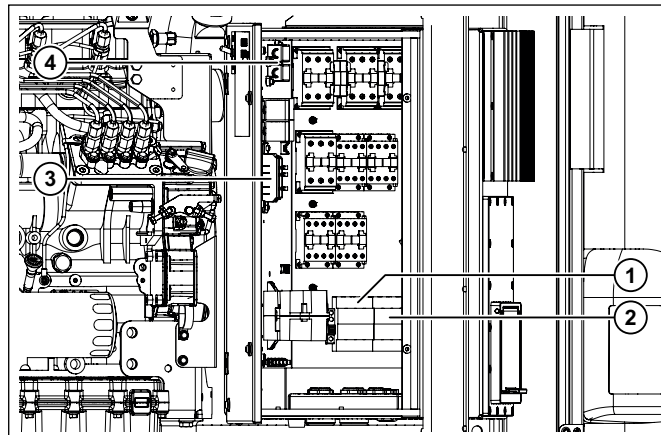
Vue d'ensemble des fusibles de la S.CU d80 et S.CU e80
